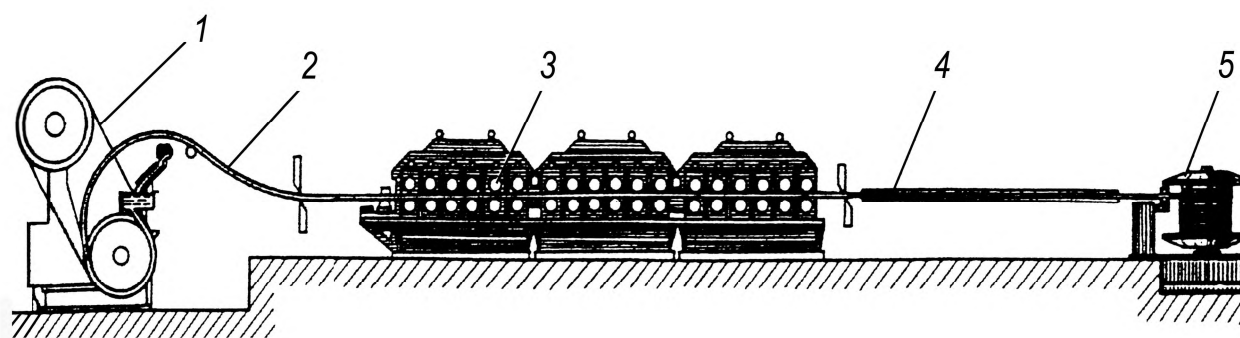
Типовая схема агрегата непрерывного литья и прокатки медной катанки:
